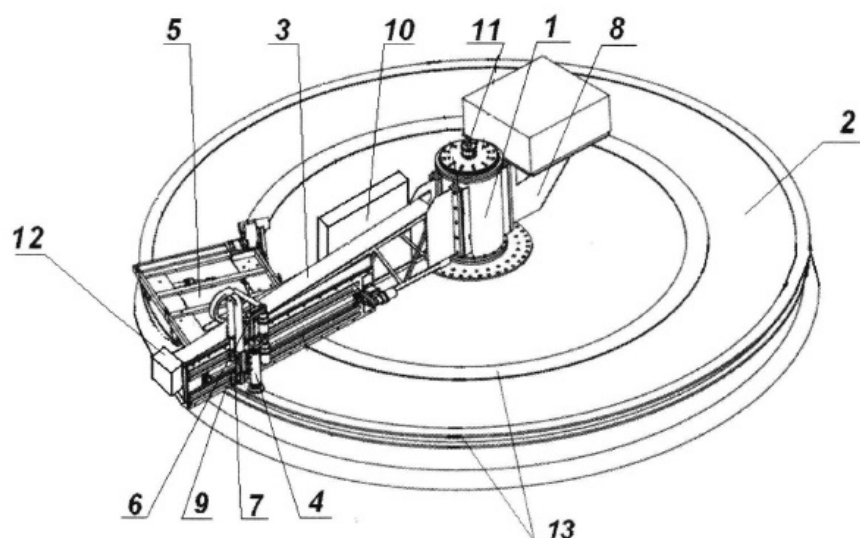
Переносной станок для обработки, преимущественно, крупногабаритных деталей [11]:
